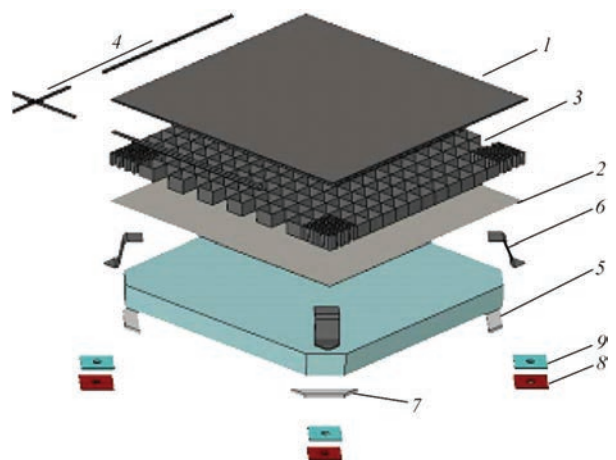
Общий вид плитки ТЗК: 1 — верхняя обшивка панели; 2 — нижняя обшивка панели; 3 — сотовый заполнитель; 4 — U-образные выштамповки; 5 — теплоизоляция; 6 — Z-образные металлические стойки системы крепления; 7 — фетровая подложка; 8 — демпфирующая прокладка из термостойкой резины; 9 — термомост
